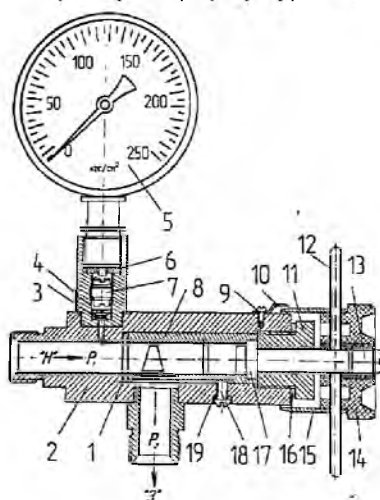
Конструктивна схема витратоміра [4]: 1, 6, 16, 19 - ущільнювальні прокладки; 2 - корпус; 3, 4 - шайба і пластина демпфера; 5 - манометр; 7 - гвинт демпфер; 8 - втулка; 9, 13, 18 - гвинт; 10 - стрілка показчик; 11 - напрямна; 12 - стержень; 14 - рукоятка; 15 - лимб; 17 - плунжер.
